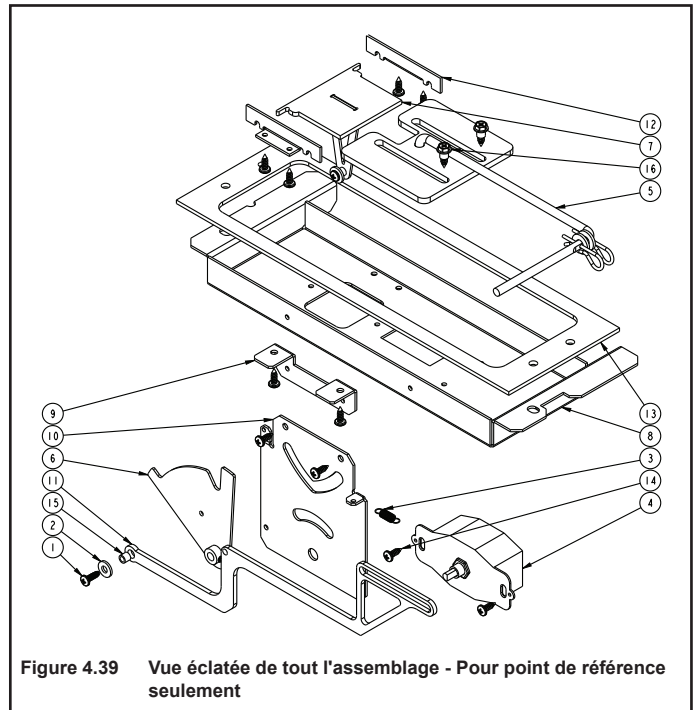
Vue éclatée de tout l'assemblage - Pour point de référence seulement
